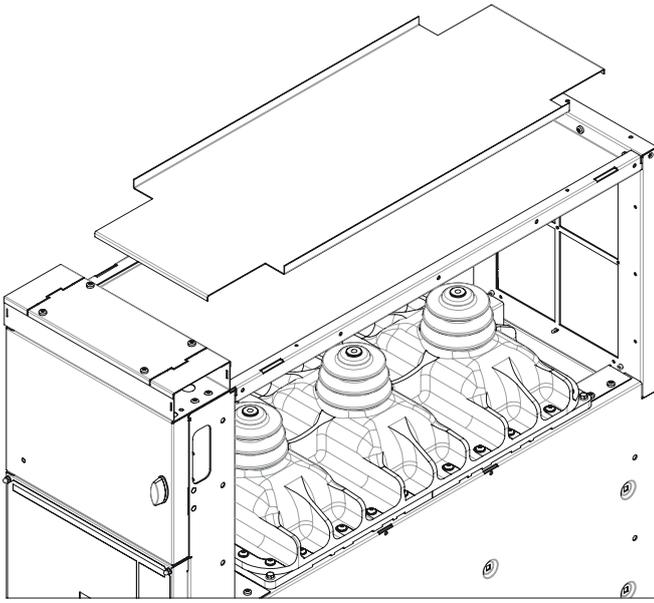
Installazione della piastra di protezione antincendio e della doppia piastra del tetto
